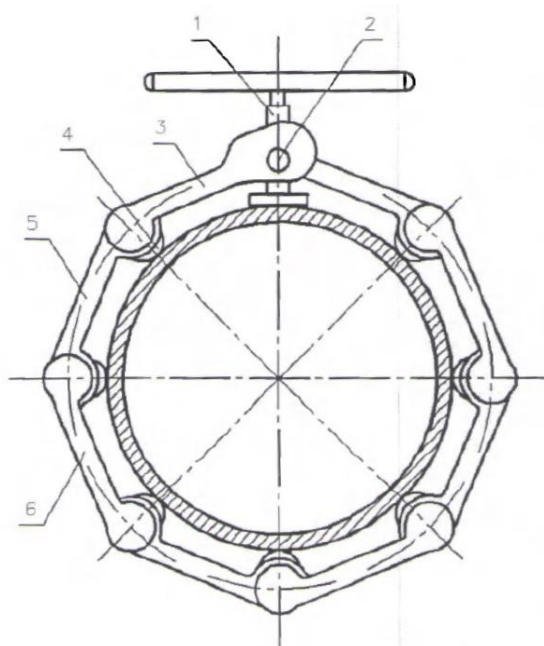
Центратор наружный с шарнирными рычагами
